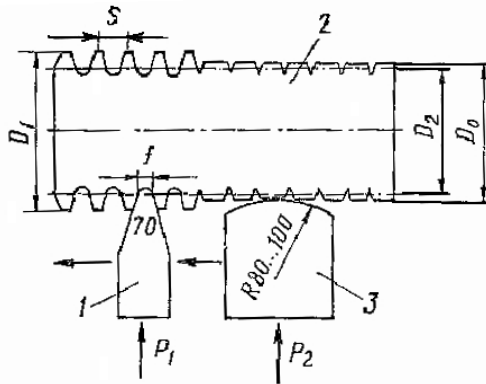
Схема відновлення вала на токарному верстаті електромеханічною обробкою: 1 – висаджувальна пластина; 2 – деталь; 3 – згладжувальна пластина
